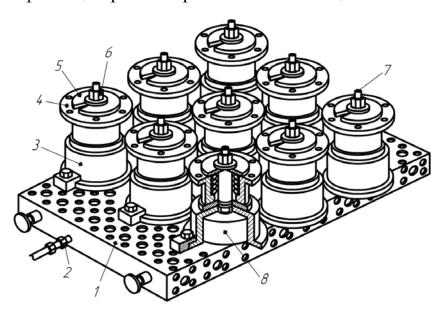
Девятиместное гидравлическое приспособление для установки фланца: 1 — плита; 2 — быстроразъемное соединение; 3 — стакан; 4 — заготовка; 5 — быстросъемная шайба; 6 — гайка; 7 — шпилька; 8 — гидроцилиндр
